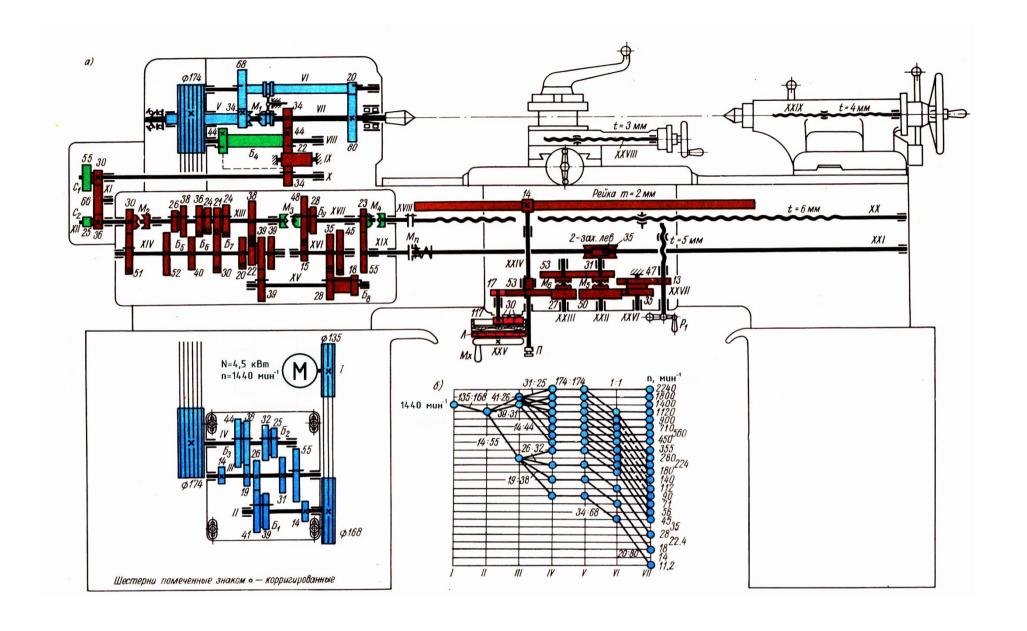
Кинематическая схема токарно-винторезного станка модели 1А616
